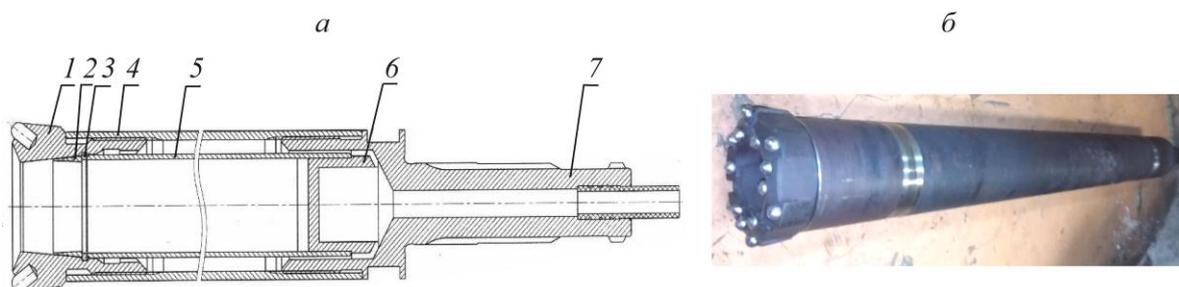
Двойной колонковый набор НДК134: *a* — схема устройства: 1 — коронка кернозаборная; 2 — керносрыватель; 3 — стопорное кольцо; 4 — труба наружная; 5 — труба керноприемная; 6 — пробка; 7 — переходник к погружному пневмоударнику; *б* — опытный образец.
